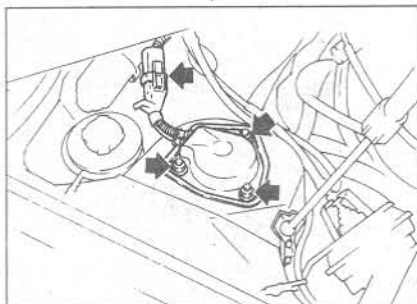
Регулируемая стойка подвески - гайки верхнего крепления и соединитель электропроводки исполнительного механизма отмечены стрелками (Глава 6)
